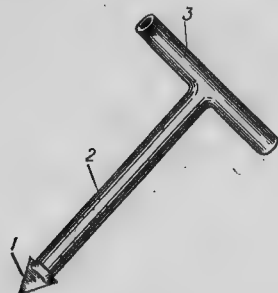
1 — наконечник; 2 — корпус; 3 — ручка
